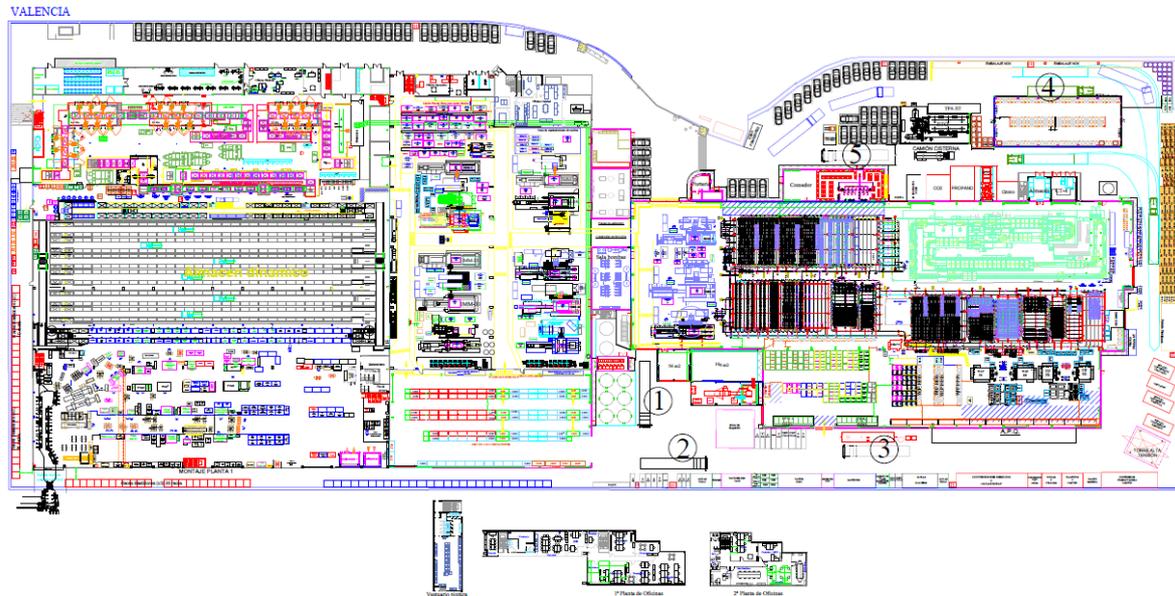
Lay Out planta Almussafes (Fuente: Plastic Omnium)
